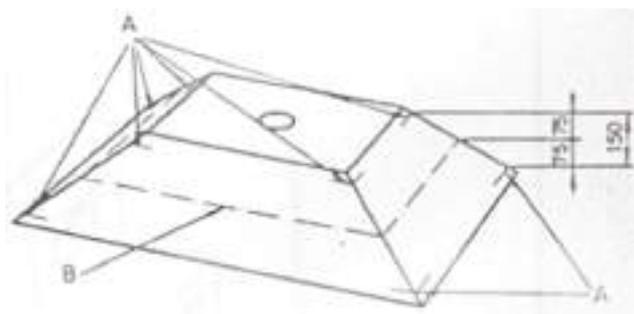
Pode ver-se nesta peça os traços A que delimitam os planos paralelos horizontais e o plano mediano B, traçado justamente a metade da distância entre esses dois planos.
